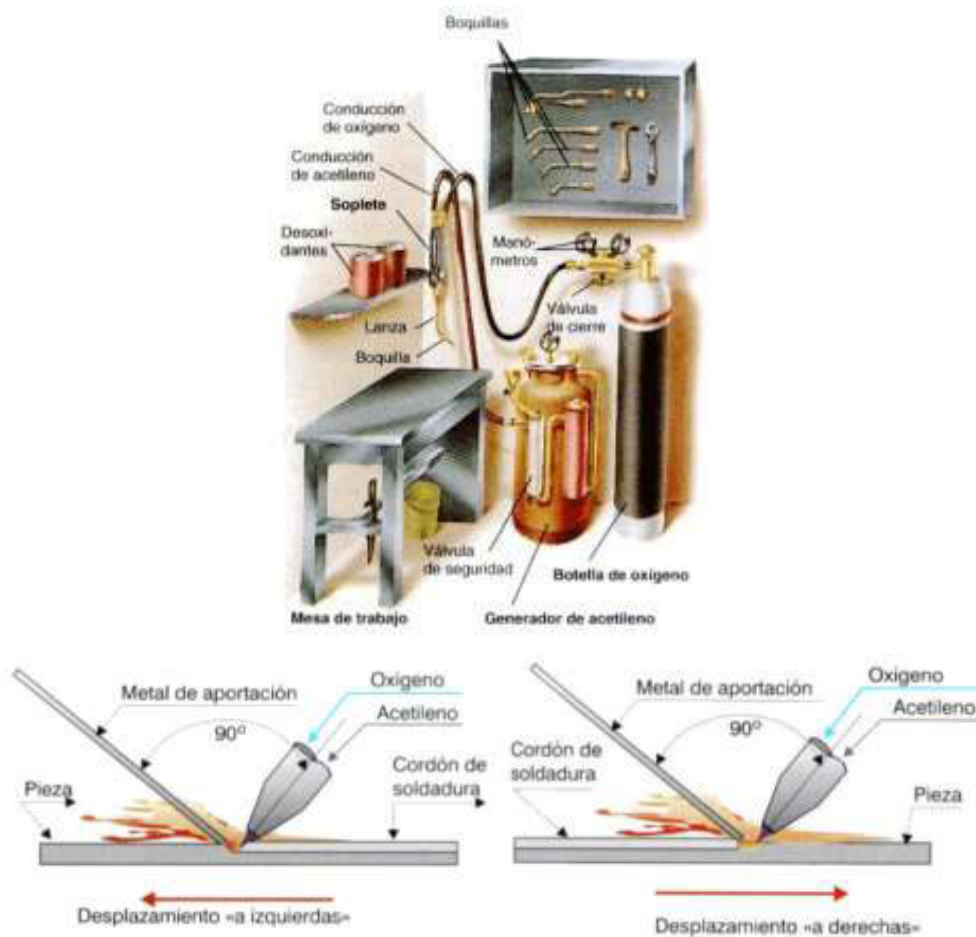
Elementos Para La Soldadura Oxiacetilénica
